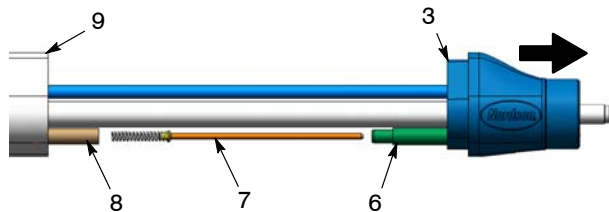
Démontage de la résistance – pistolets à fixation sur tube
